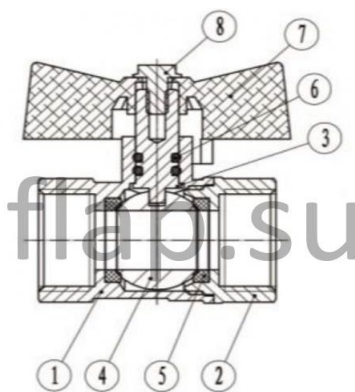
Чертеж крана с деталями из паспорта завода изготовителя:
